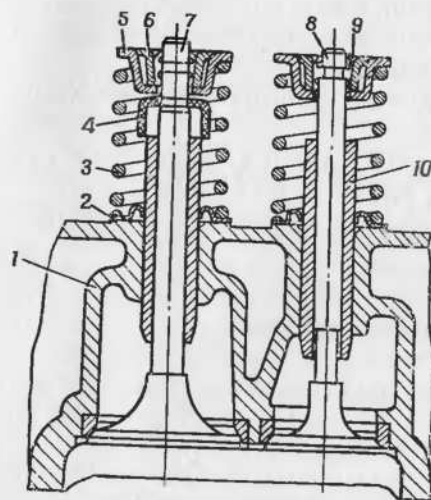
Установка пружин клапанов: 1 — головка цилиндра; 2 — опорная шайба; 3 — пружина клапана; 4 — колпачок; 5 — тарелка пружины клапана; 6 — втулка тарелки; 7 — клапан впускной; 8 — клапан выпускной; 9 — сухарь; 10 — направляющая втулка
